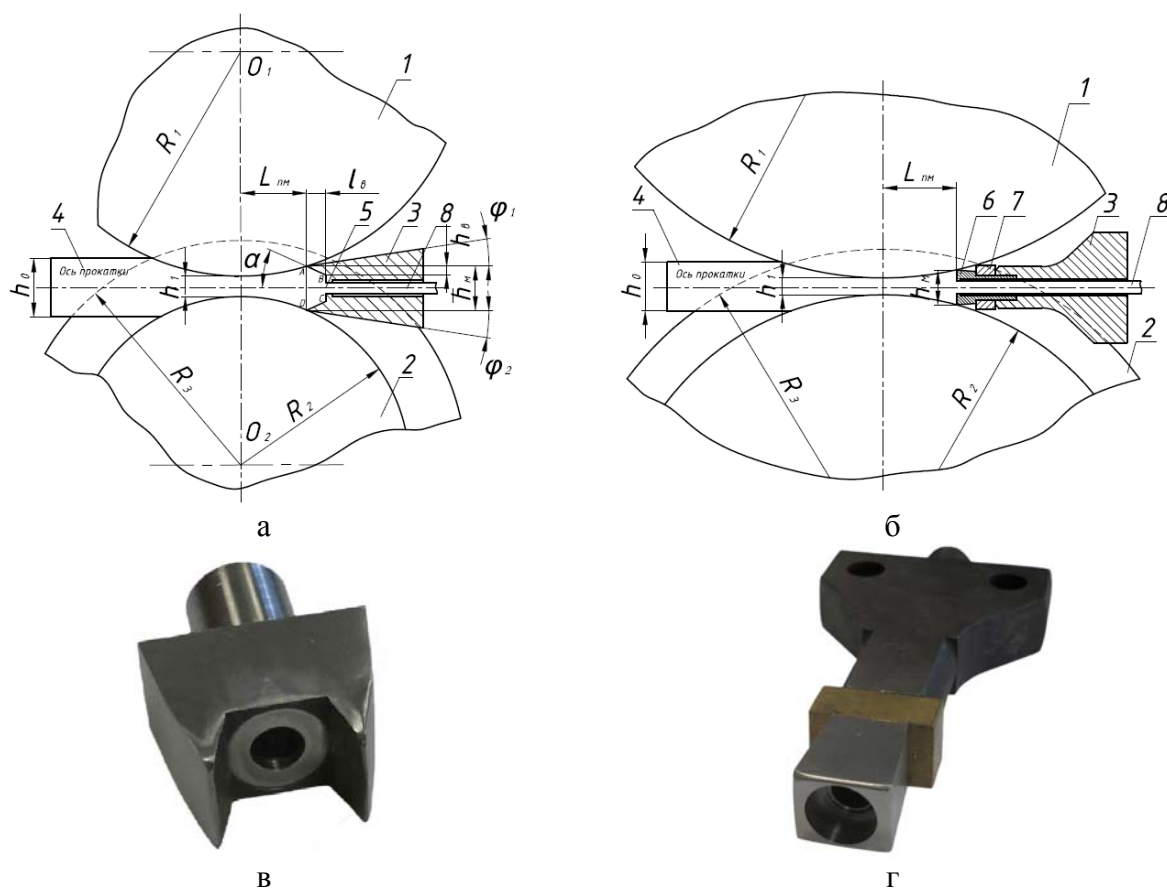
Устройства для совмещенной прокатки и прессования по патенту РФ №138590 (а) и РФ №139085 (б) и вид матричного инструмента (в, г): 1 - валок с выступом; 2 - валок с канавкой; 3 - матрица; 4 - заготовка; 5 - трапециевидная выемка; 6 - калибрующая вставка; 7 - антифрикционная вставка; 8 - изделие
